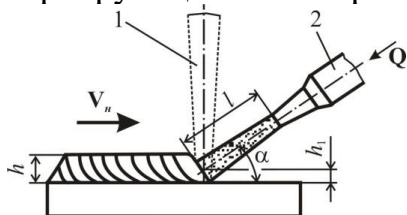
Схема процесса газопорошковой лазерной наплавки:
